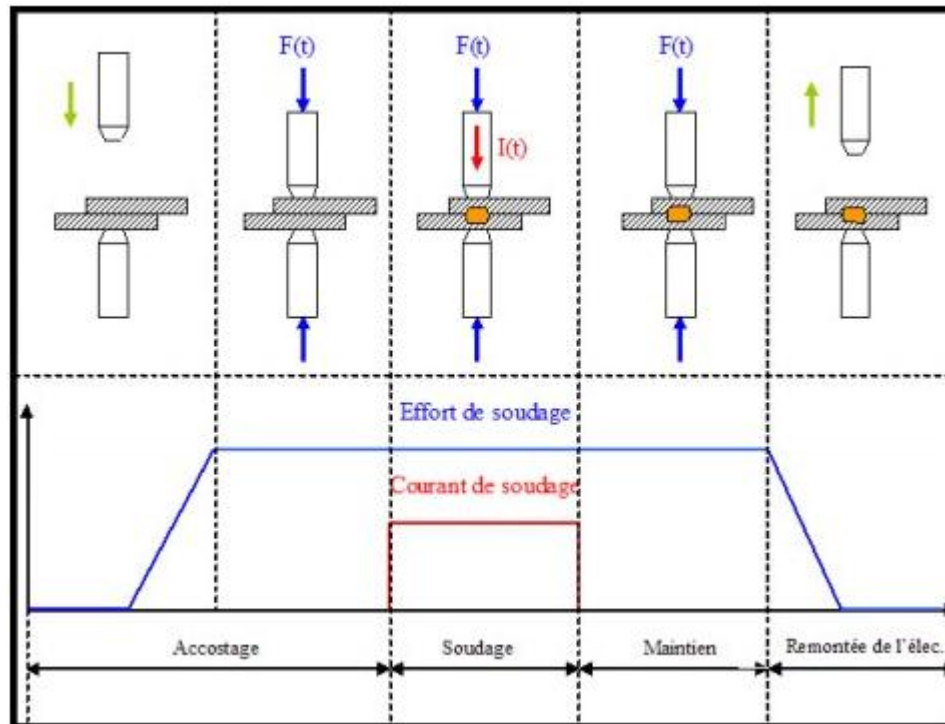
Schéma des étapes successives du soudage par points [3].
